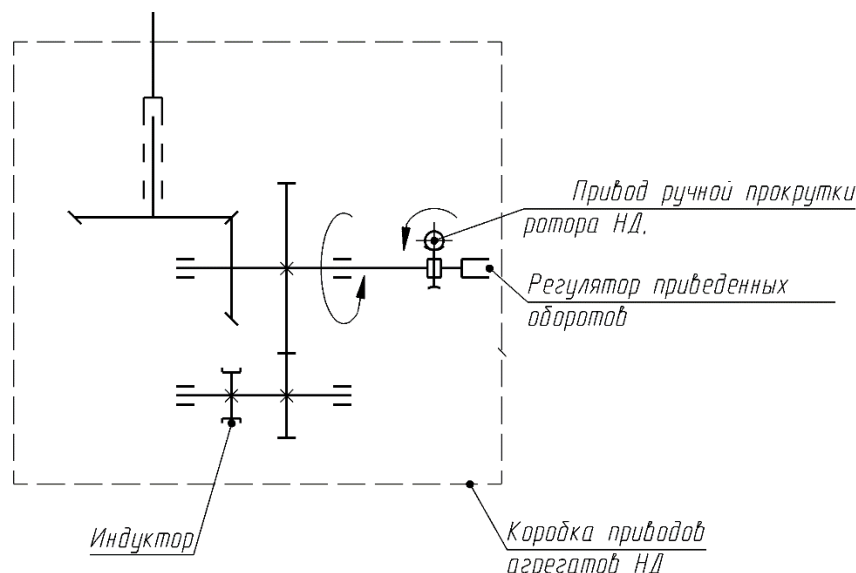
Кинематическая схема коробки приводов агрегатов НД
